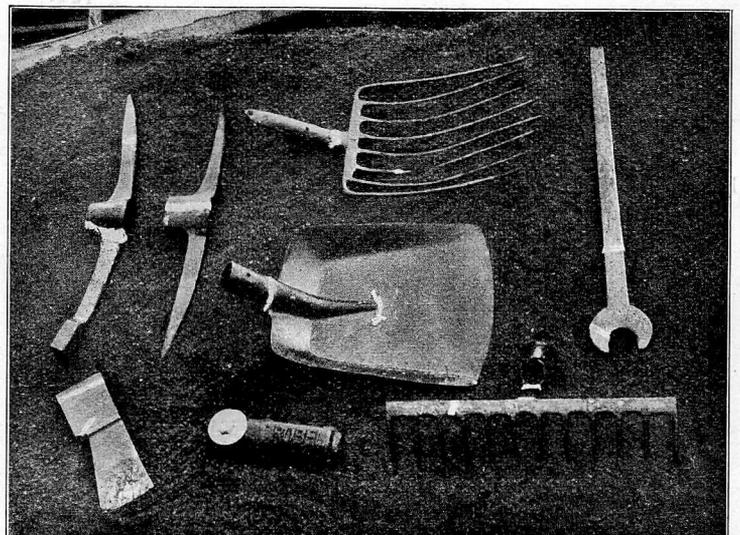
Geschweißte Werkzeuge und Geräte.
